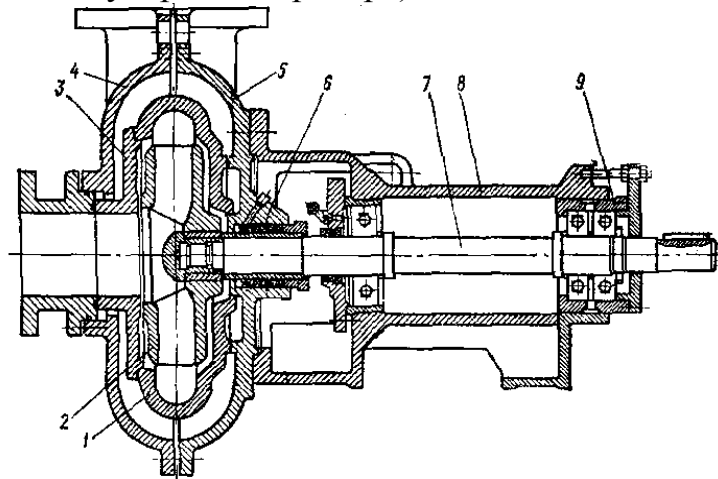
Двокорпусний ґрунтовий насос: 1 – внутрішній корпус; 2 – робоче колесо; 3 – захисний диск; 4 – передня половина корпусу; 5 – задня половина корпусу; 6 – сальник; 7 – вал; 8 – опорний кронштейн; 9 – стакан для регулювання осьового переміщення
